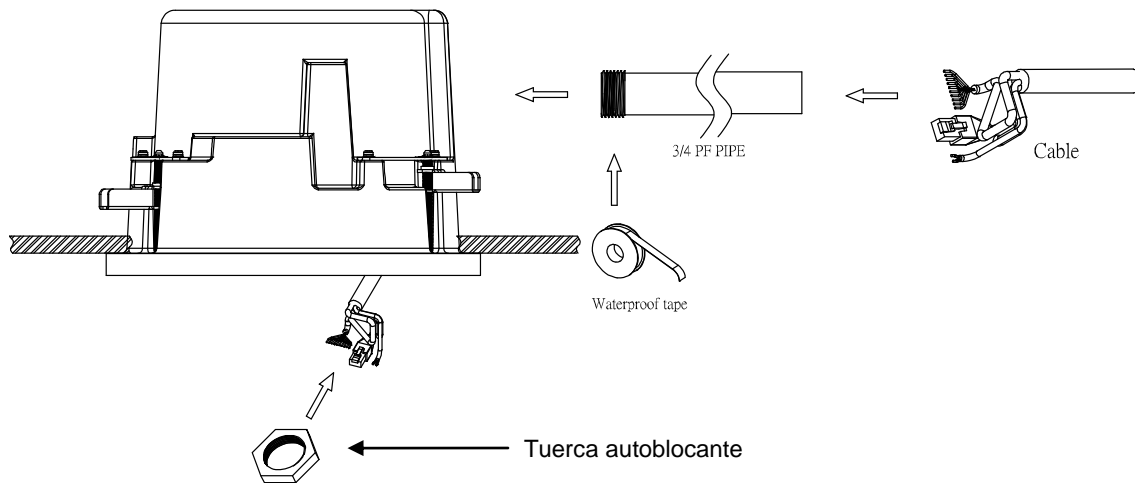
CABLEADO EMPOTRADO EN EL TECHO PARA EXTERIORES
